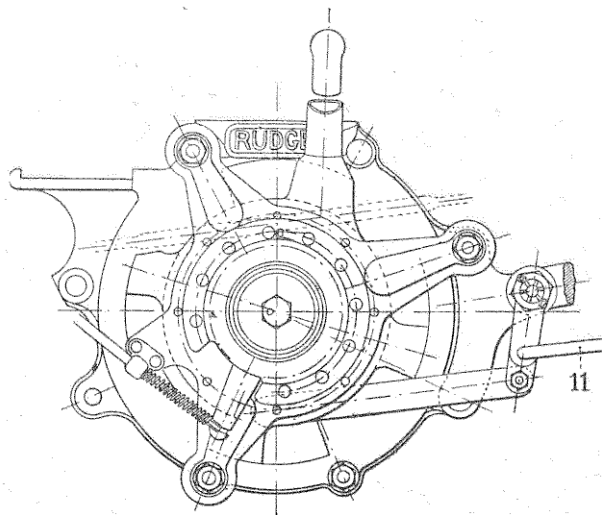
Changement de vitesse *Rudge Multi*. Vue de face de la poulie motrice, avec le carter du moteur.
